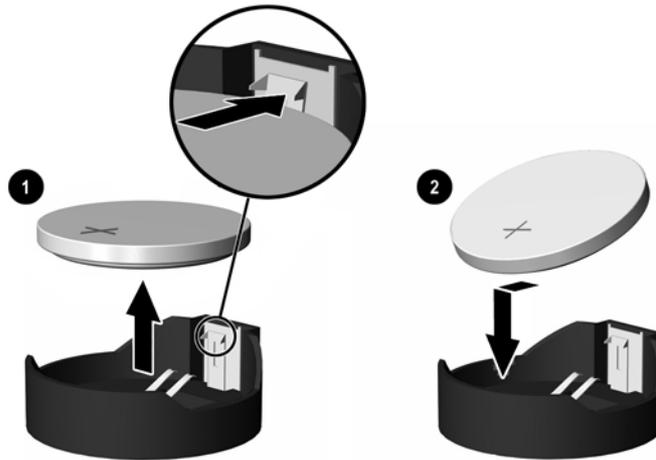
Extracción y reemplazo de una batería plana (Tipo 2)
